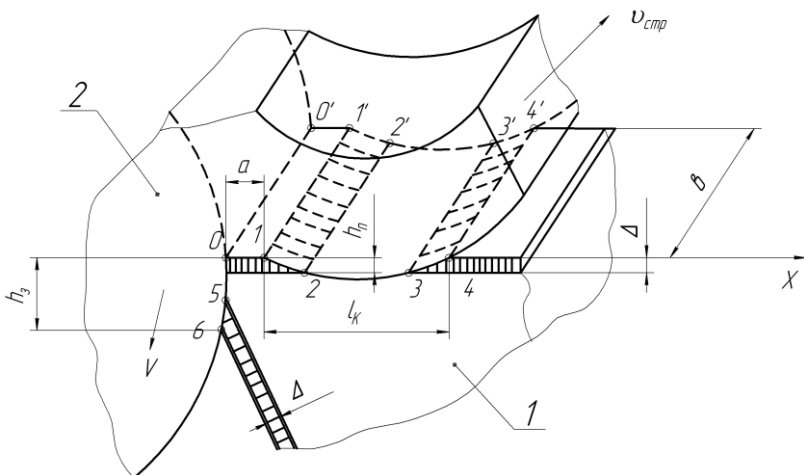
Схема контакта при резании металлов: h_3 - износ по задней поверхности инструмента; l_k , b , h_n -длина, ширина и глубина лунки износа соответственно; a - размер полочки; Δ - толщина покрытия; 1-инструмент; 2-заготовка
